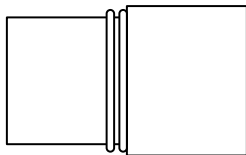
Dvojitá svarová housenka. Viditelná a jednolitá
